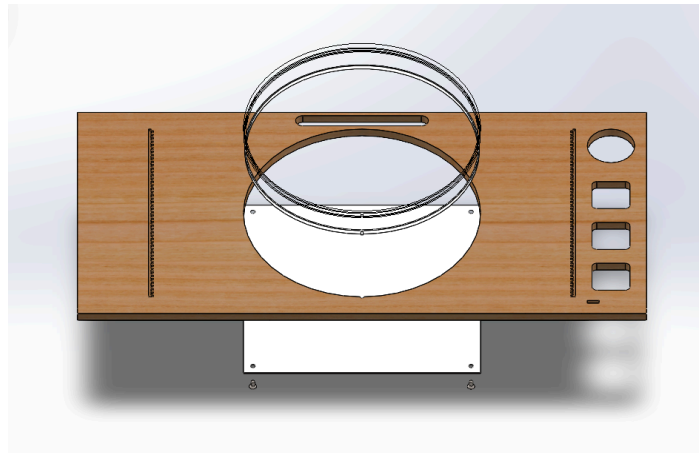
Explosión de los componentes del disco de calco (Fuente: Elaboración Propia)
